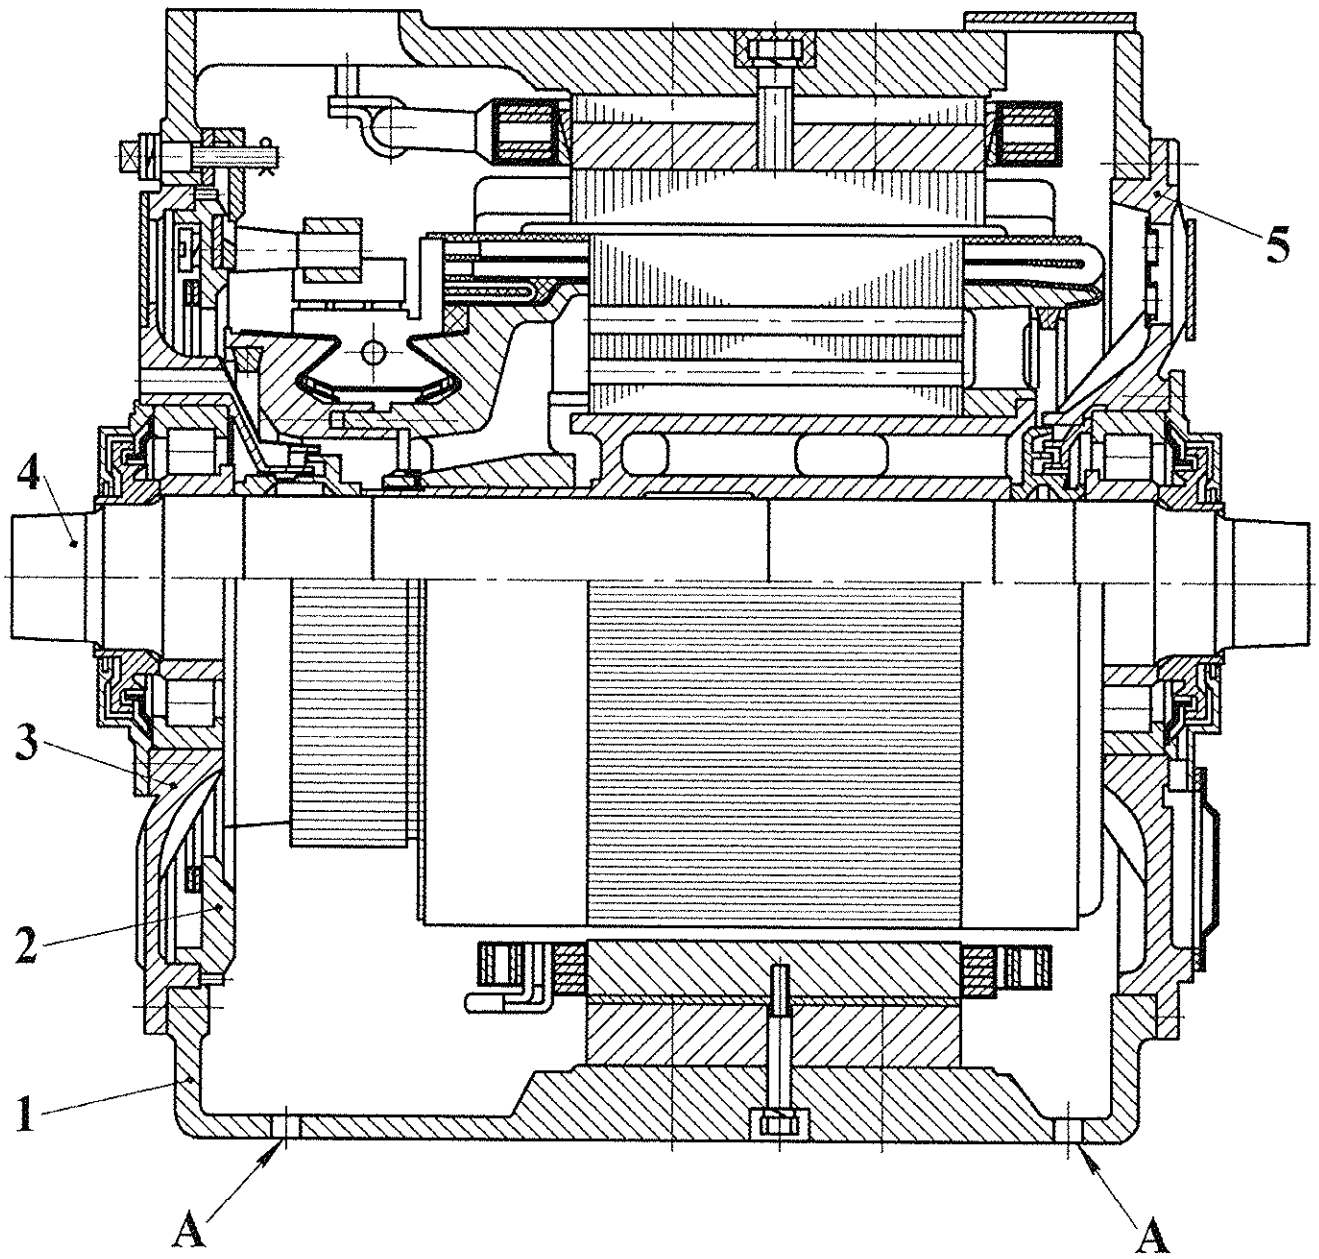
Продольный разрез тягового двигателя НБ-514Б
